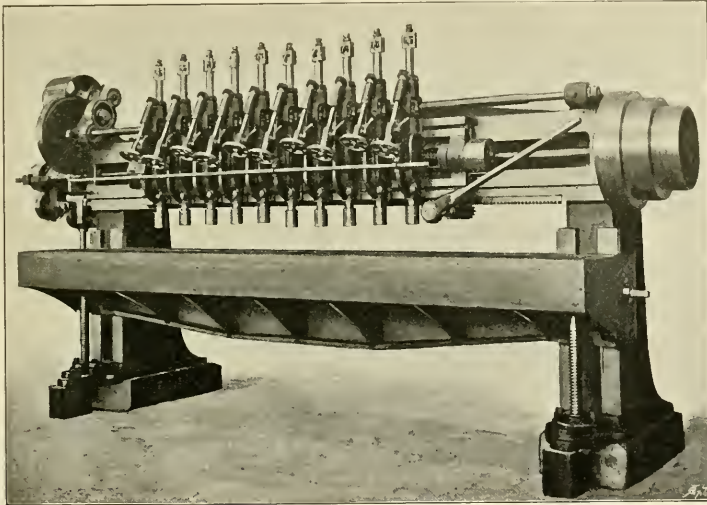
Bohrmaschine mit zehn Bohrspindeln.
